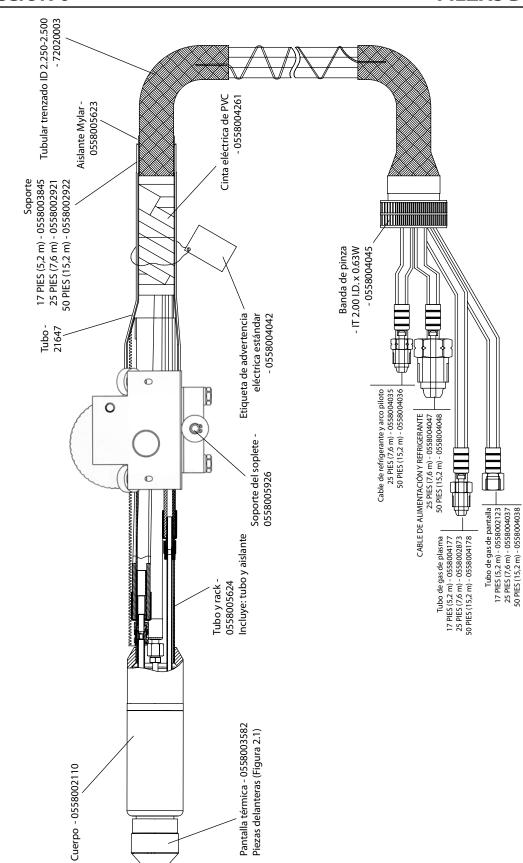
Piezas de recambio – Montaje de soplete PT26 "SL" In-Line
